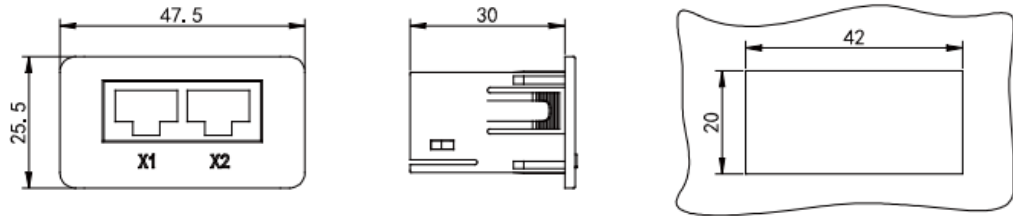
Внешний вид и габаритные размеры модуля коммутации Z3/Z4
